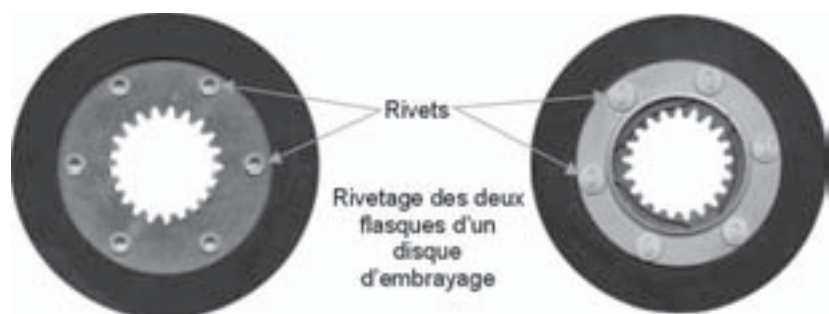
Rivetage des deux flasques d'un disque d'embrayage.
